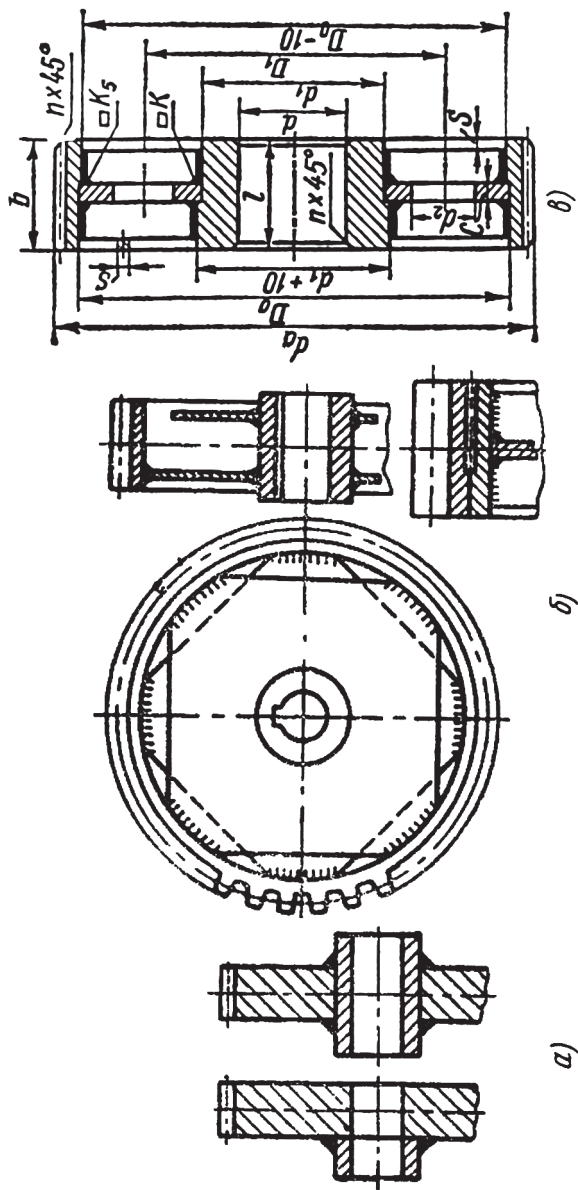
Сварные цилиндрические зубчатые колеса
